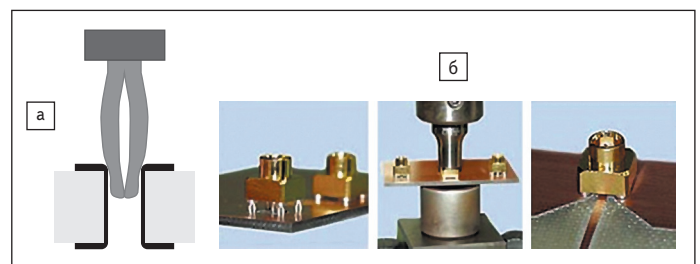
а) Пружинящий вывод; б) пресовая посадка соединителя компании IMS в отверстия печатной платы
